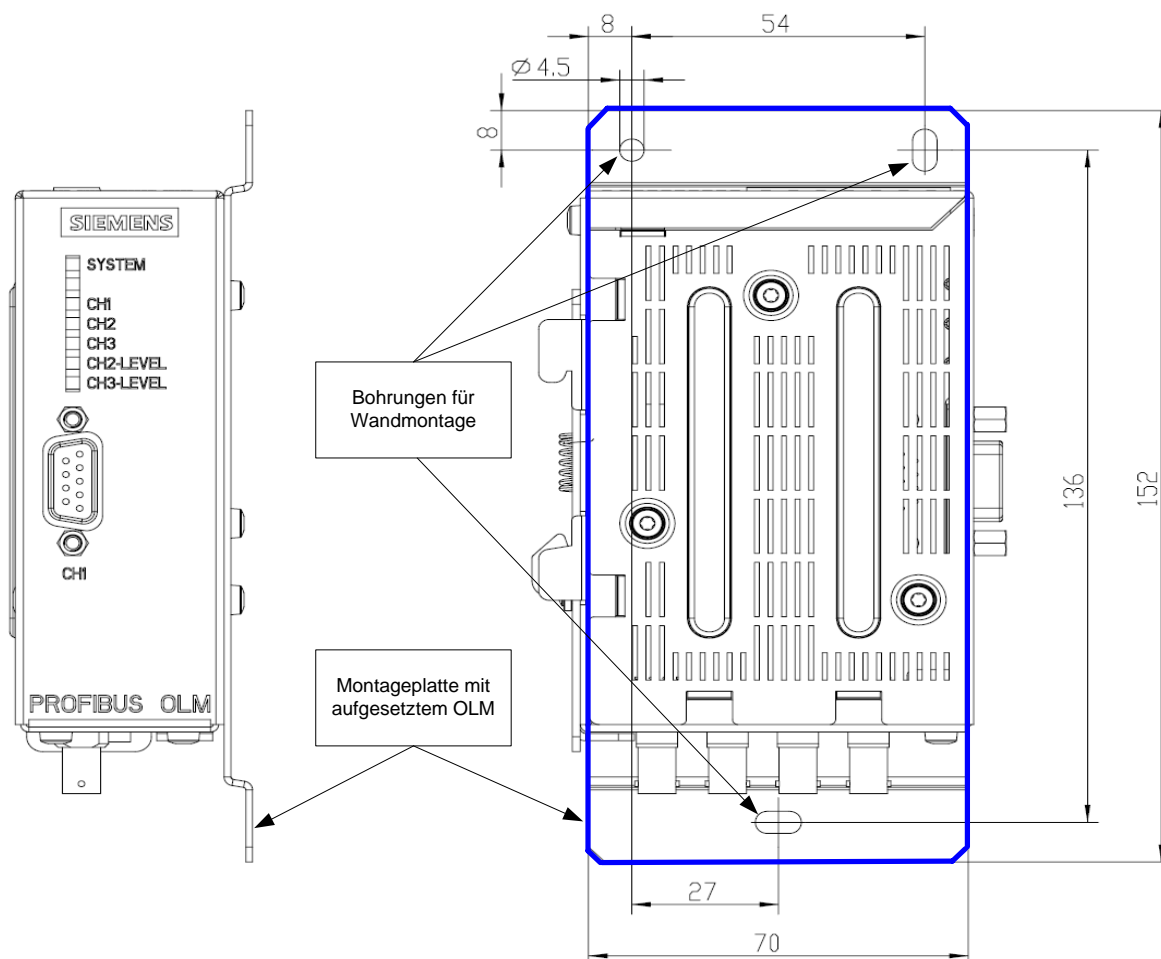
Montage eines Moduls mit einer Montageplatte
